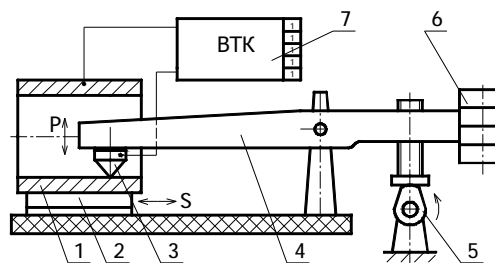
Принципова схема обробки внутрішньої поверхні втулки дискретною ППД: 1-втулка; 2-напрямна; 3-інструмент-індентор; 4-важель; 5-кулачок; 6-вантажі; 7- вимірювач тривалості контакту.
